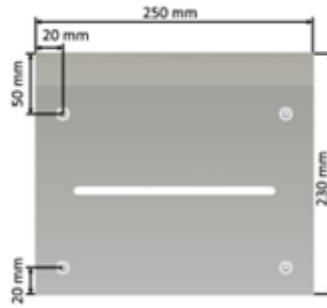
Superficie A de la sección de ensayo (donde se sitúan las agarraderas).
